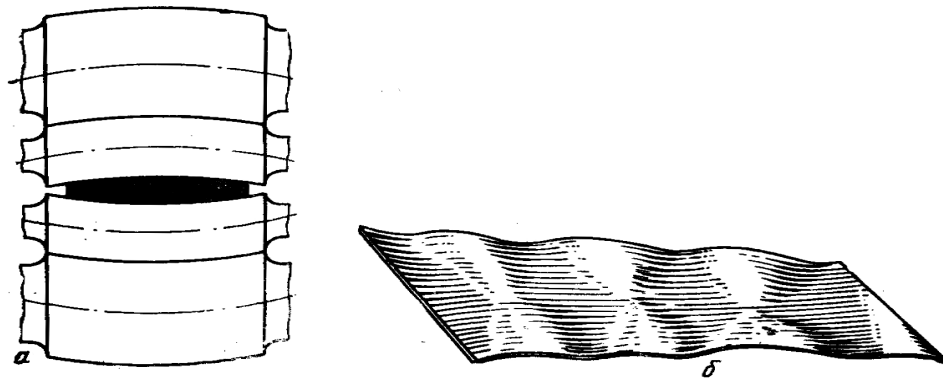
Вплив циліндричної бочки валка на якість викочування й поверхні штаби
